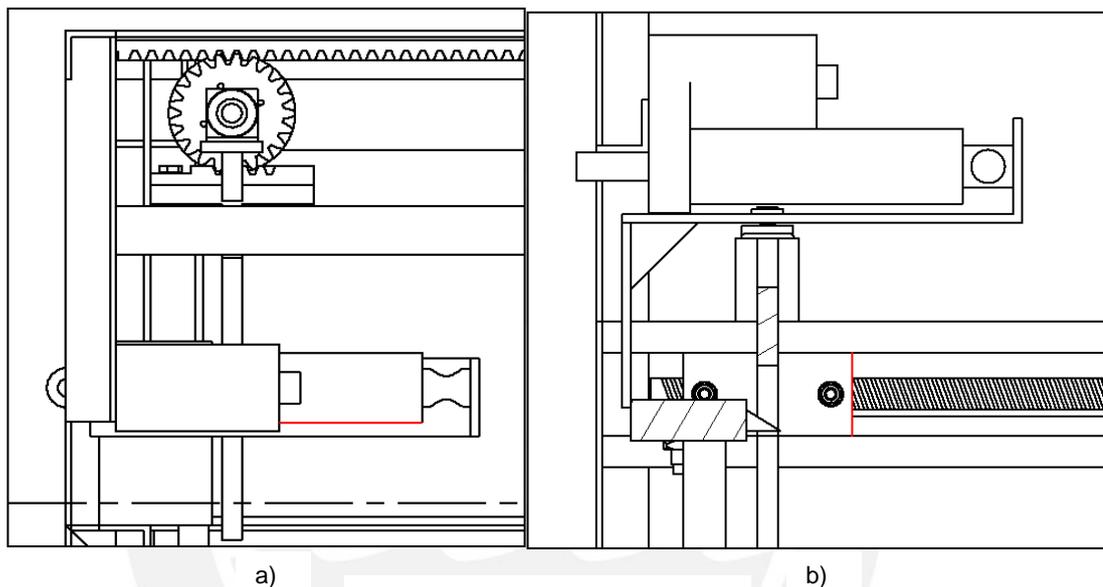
Vista de planta(a) y de detalle del empuje del pollo (b)
